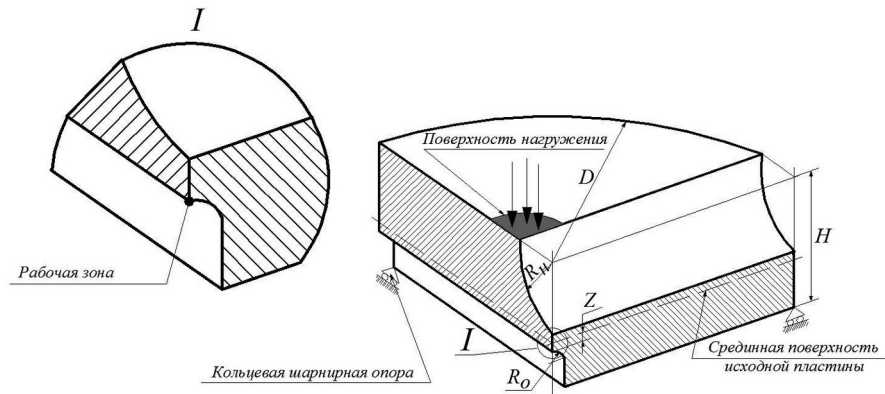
Геометрические параметры пластинчатого образца-прототипа:
